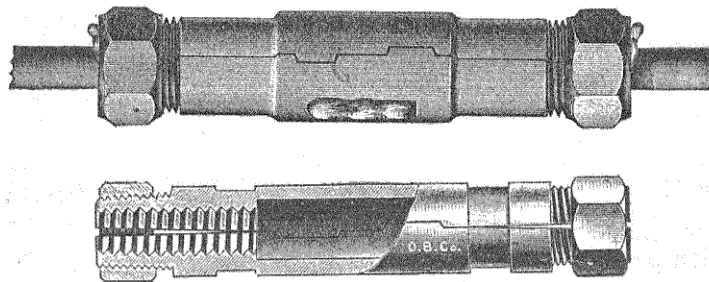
et 156. — Manchon d'assemblage pour fil de feeder.
